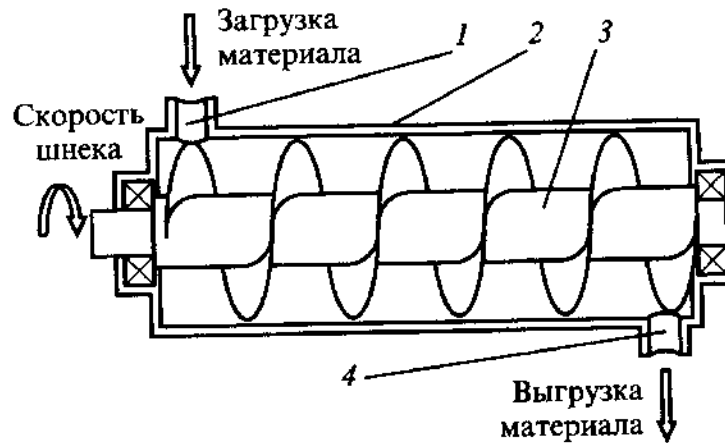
Шнековый конвейер: 1 - загрузочный люк; 2 - корпус; 3 - шнек; 4 - разгрузочный люк
